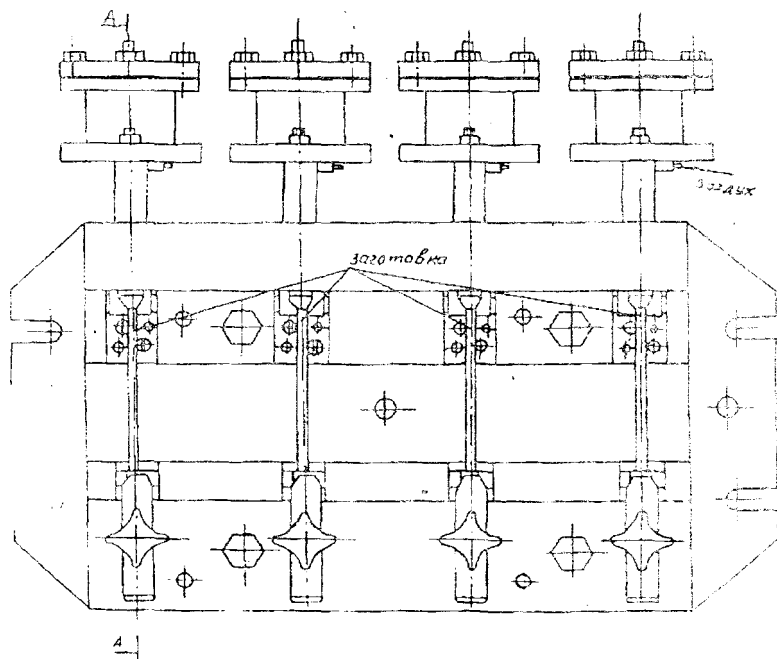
Многоместное фрезерное приспособление для обработки лопаток компрессора
